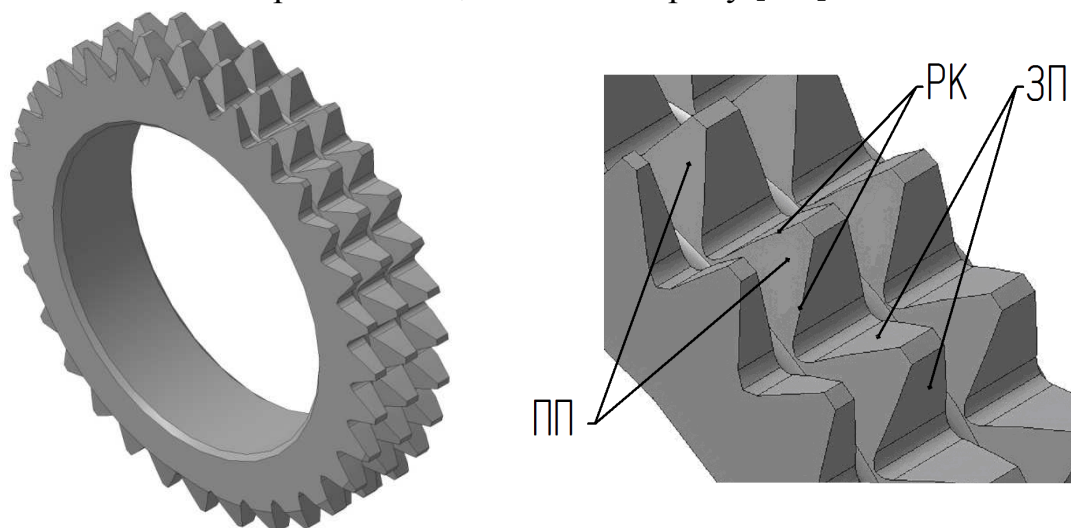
Твёрдотельная модель шевера-прикатника для зубообработки ЦЗК с выделением элементов режущих зубьев
